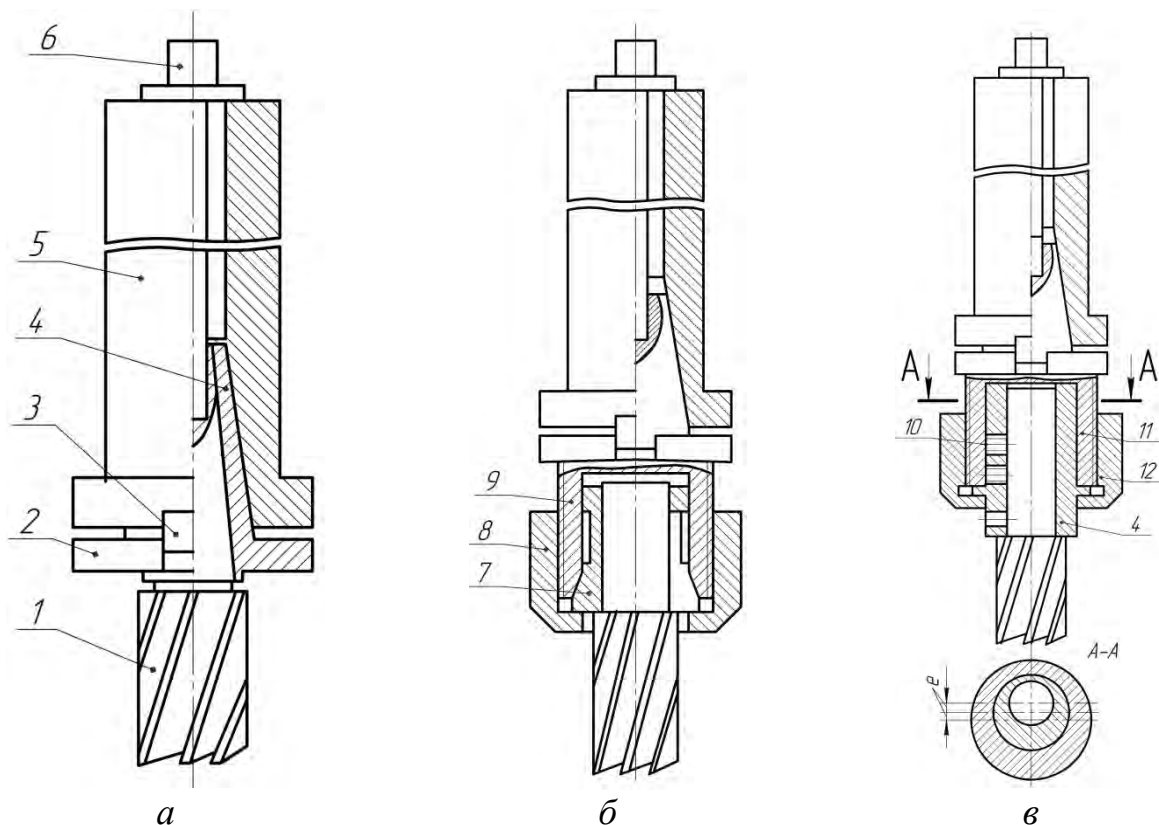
Установка концевых фрез: 1 – фреза; 2 – переходная (установочная) втулка; 3 – торцовая шпонка; 4 – конусная часть переходной втулки; 5 – вертикальный шпиндель станка; 6 – тяга; 7 – цанга; 8 – гайка; 8 – корпус цангового патрона; 10 – винт; 11 – корпус патрона с регулируемым эксцентриситетом; 12 – колпачковая гайка
